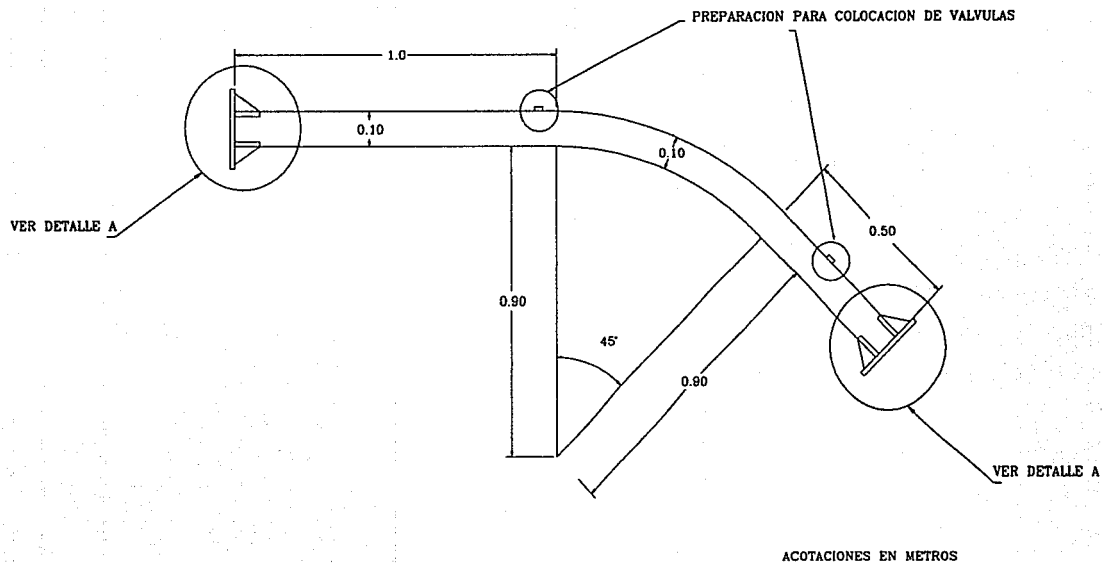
DIMENSIONES DE LA PIEZA DE ACRILICO
